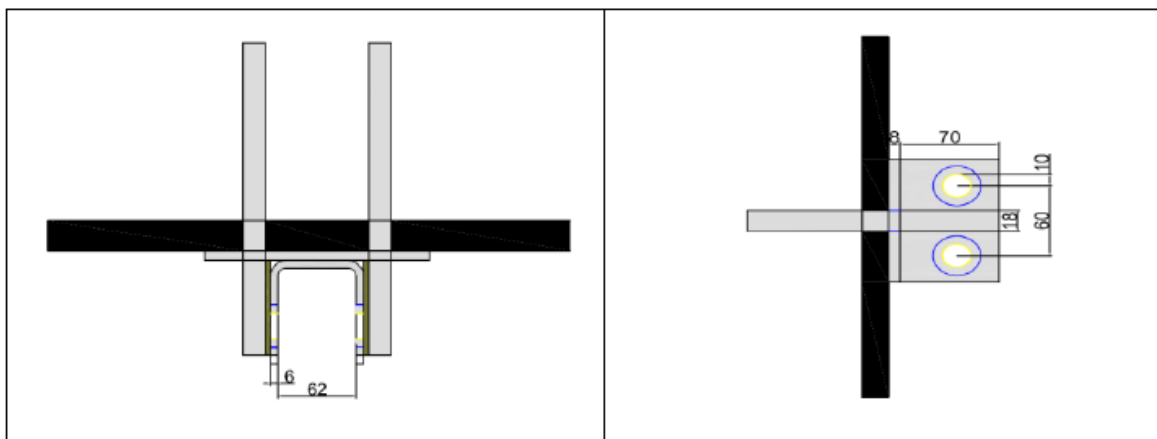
Vista en planta y elevación de estructura de soporte de pesos (Santos, 2018)
